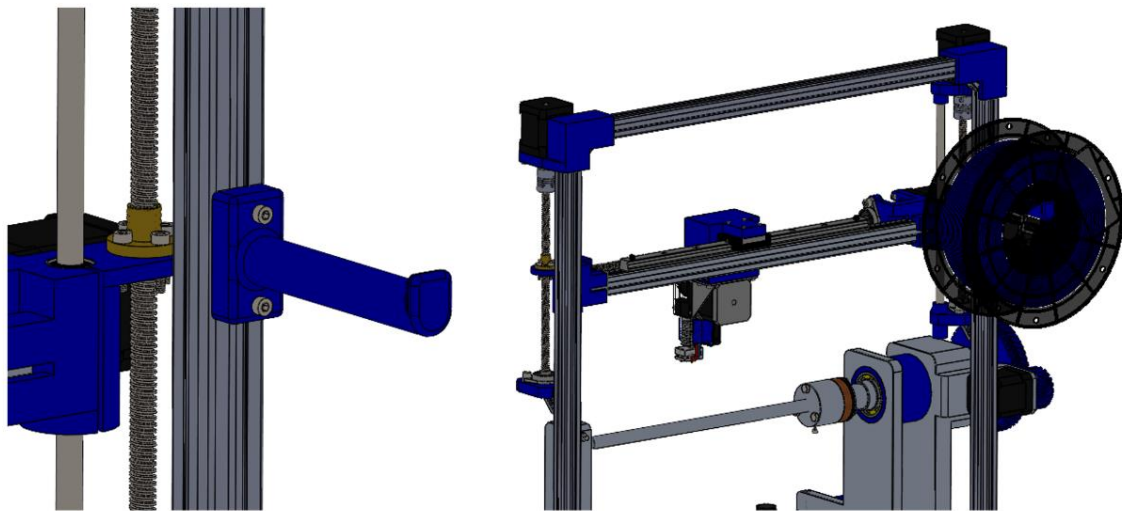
Visão geral do suporte de bobine inicialmente proposto
